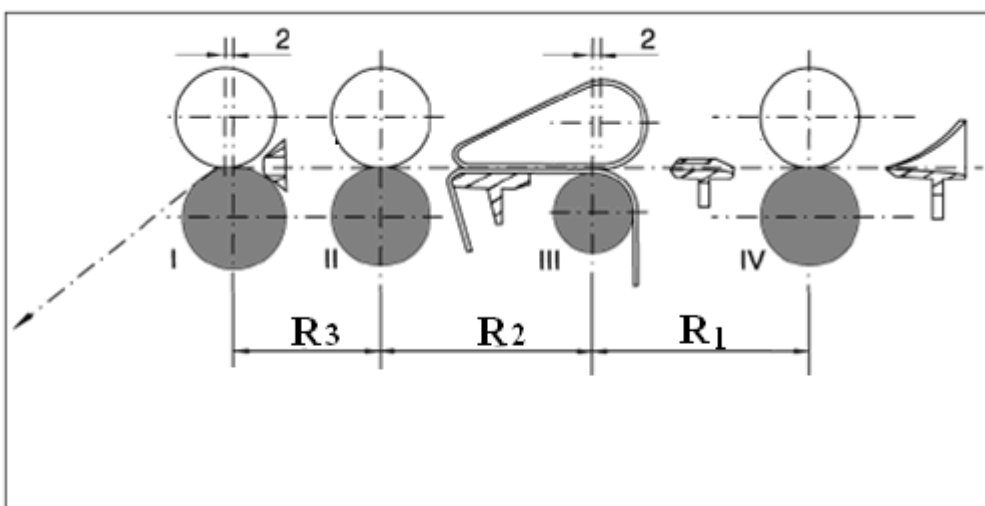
Общий вид трехцилиндрового двухремешкового вытяжного прибора
